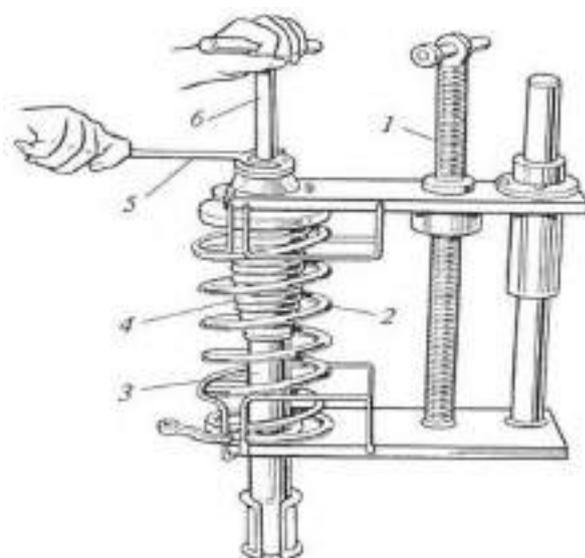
Установка телескопической стойки в приспособление для разборки: 1 — винт приспособления; 2 — пружина; 3 — амортизаторная стойка; 4 — чехол; 5 — державка; 6 — торцевой ключ
